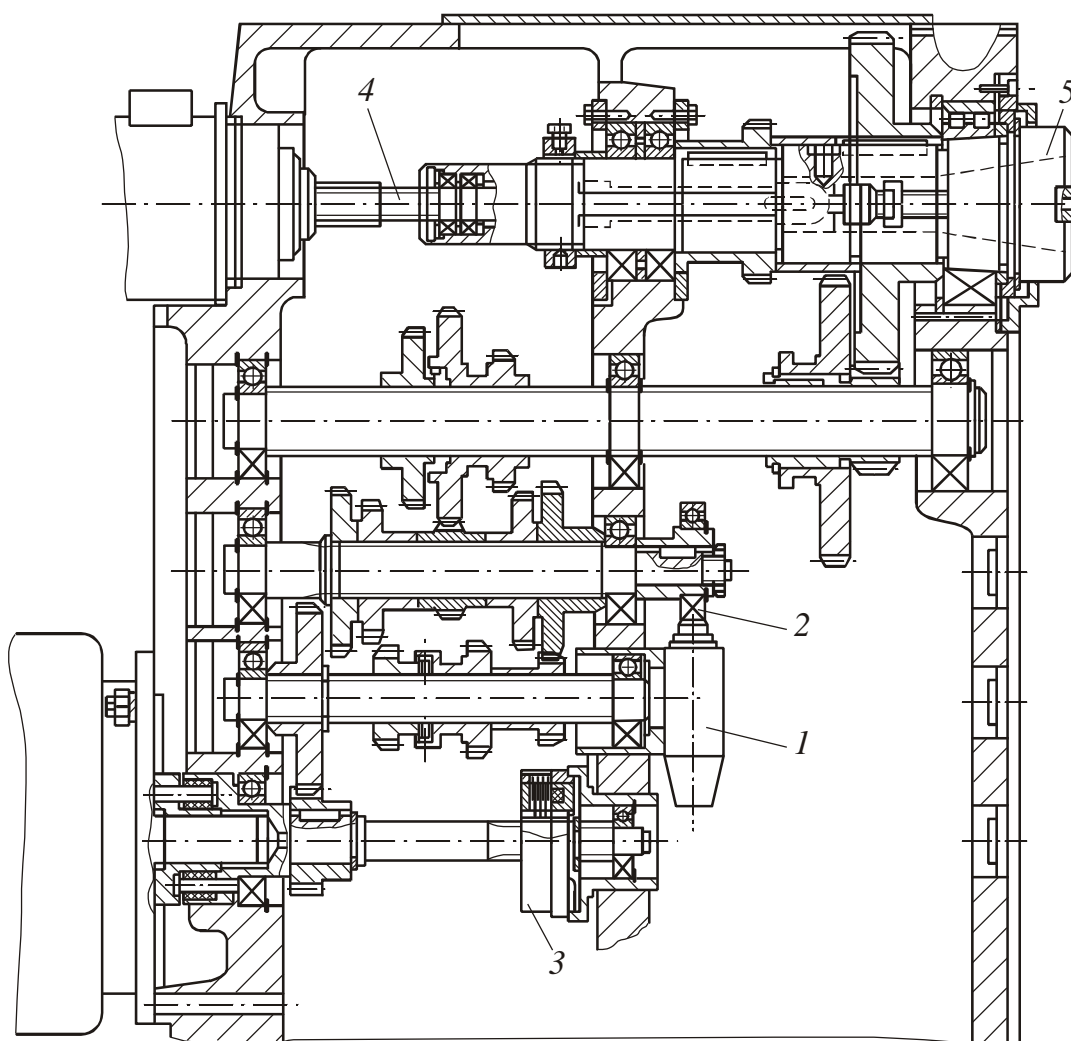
Привод главного движения горизонтально - фрезерного станка
